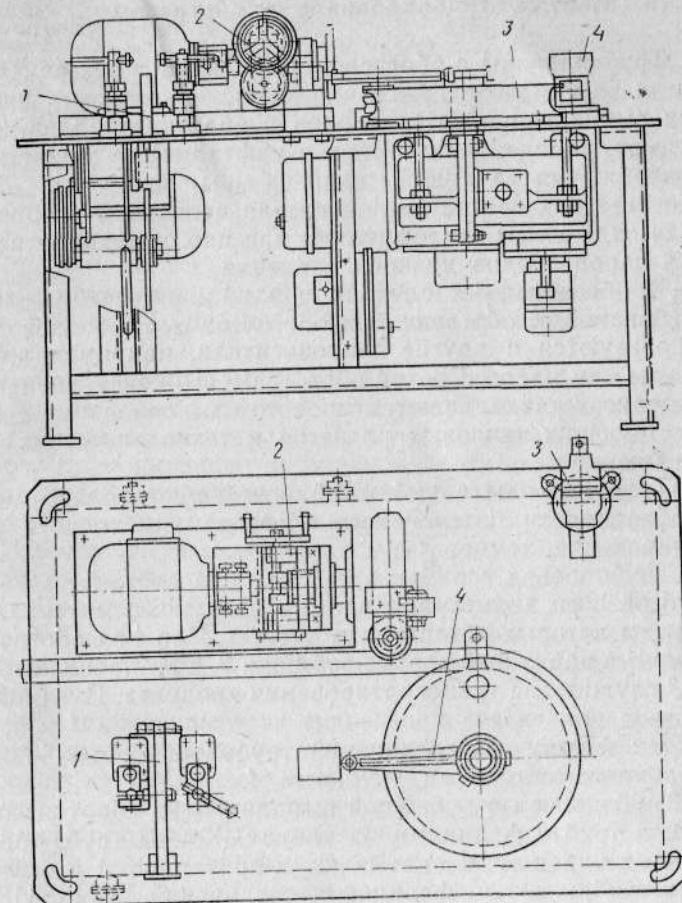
Установка СГ-60 для изготовления деталей и узлов гидравлических систем
